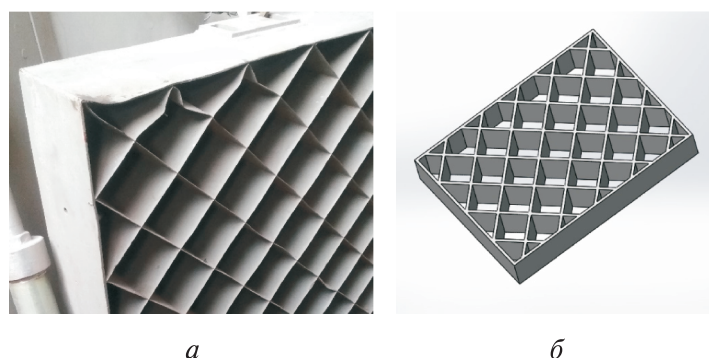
Общий вид решетчатого руля баллистической ракеты (а) и ЛСЗ (б)
